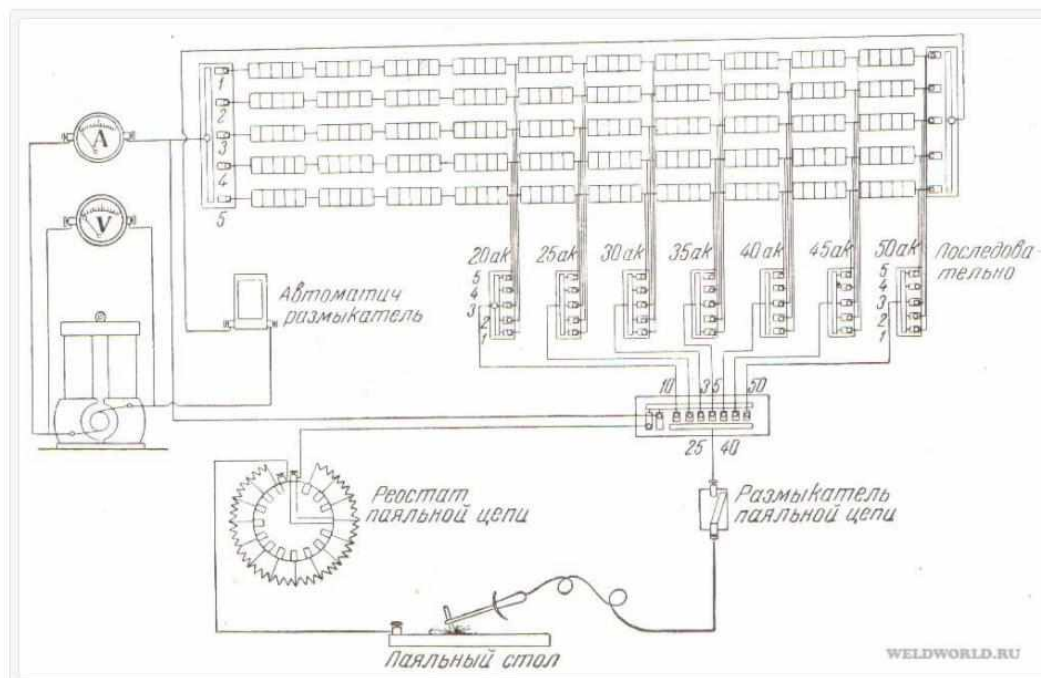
Circuito de potência de Benardos para a soldagem a arco elétrico – weldworld.ru
